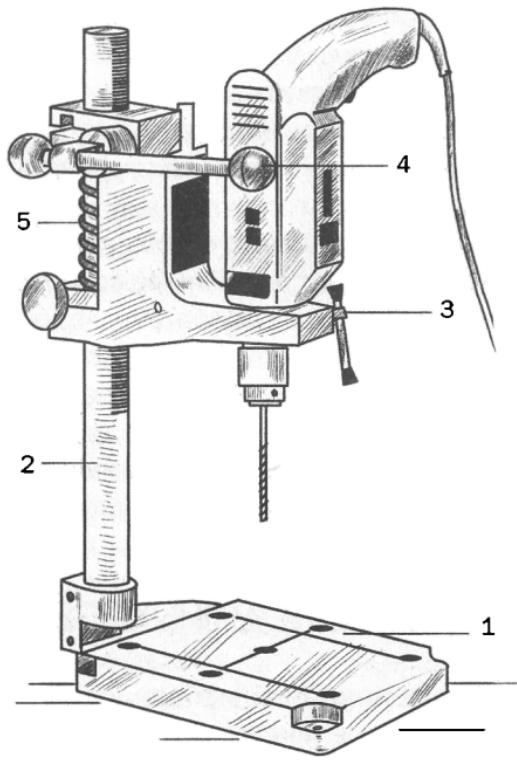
Сверлильный станок в миниатюре: 1 — станина; 2 — вертикальная штанга; 3 — зажим дрели; 4 — рычаг подачи; 5 — возвратная пружина
